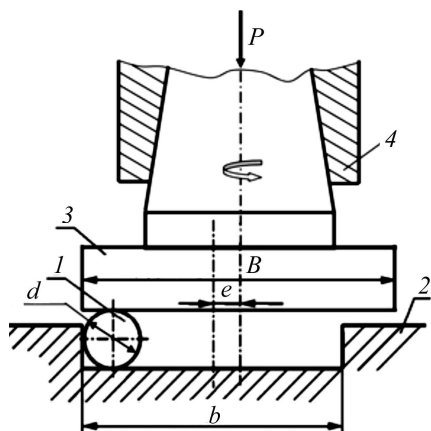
Схема накочування сферичної заготовки плоскими поверхнями:
